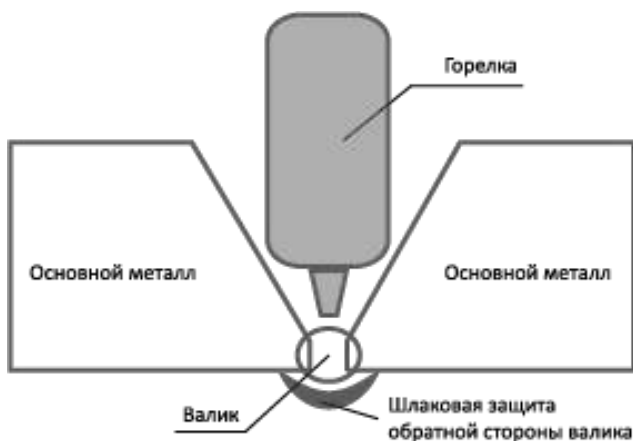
Сквозное проплавление кромок и зазор между кромками позволяют жидкому шлаку стечь к обратной стороне корня шва и равномерно покрыть проплавленный валик
